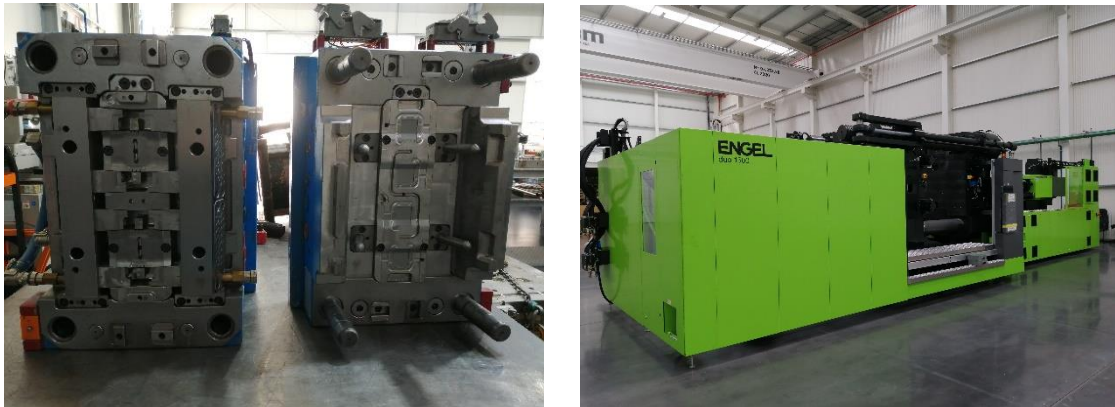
Imagem de um molde de injeção de polímeros e da máquina de injeção.
